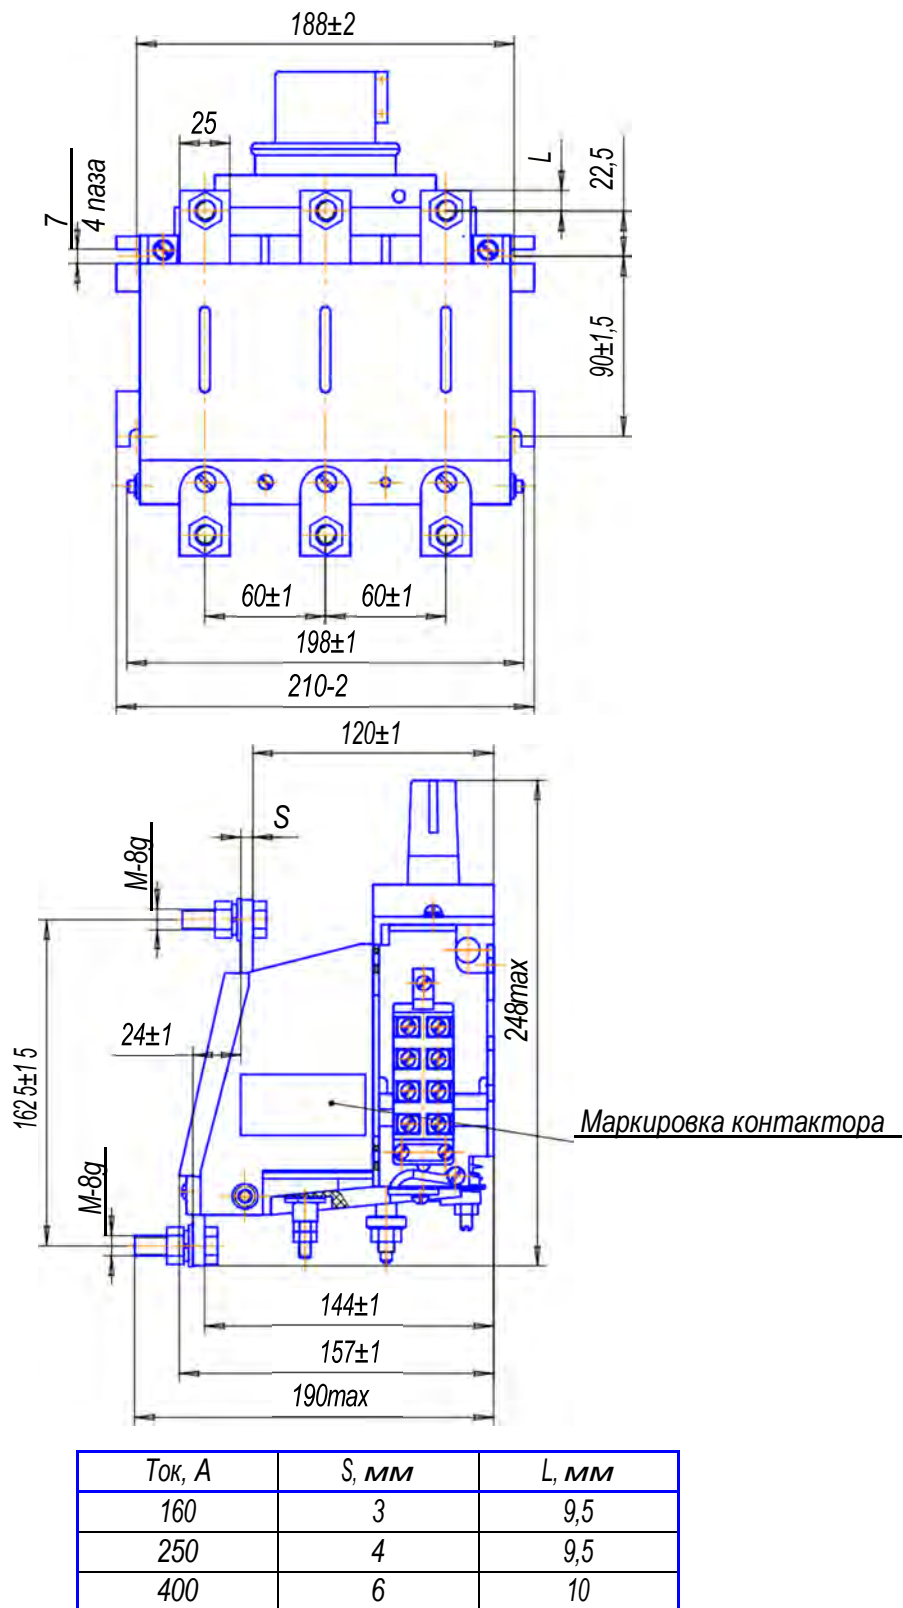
Габаритный чертёж контактора общепромышленного исполнения
